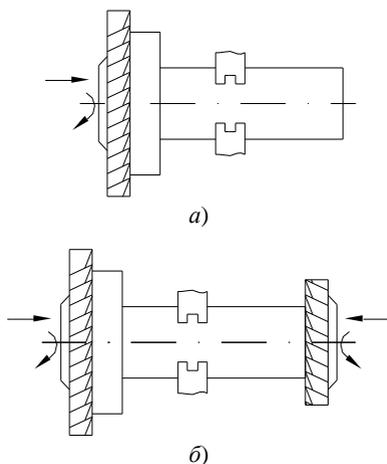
Варианты фрезерования торцов заготовки за два (а) и один (б) установка
